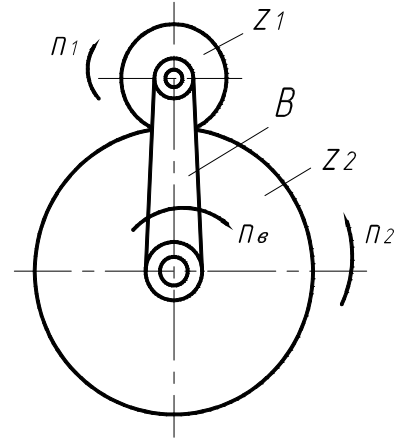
Планетарный суммирующий механизм с цилиндрическими колесами
